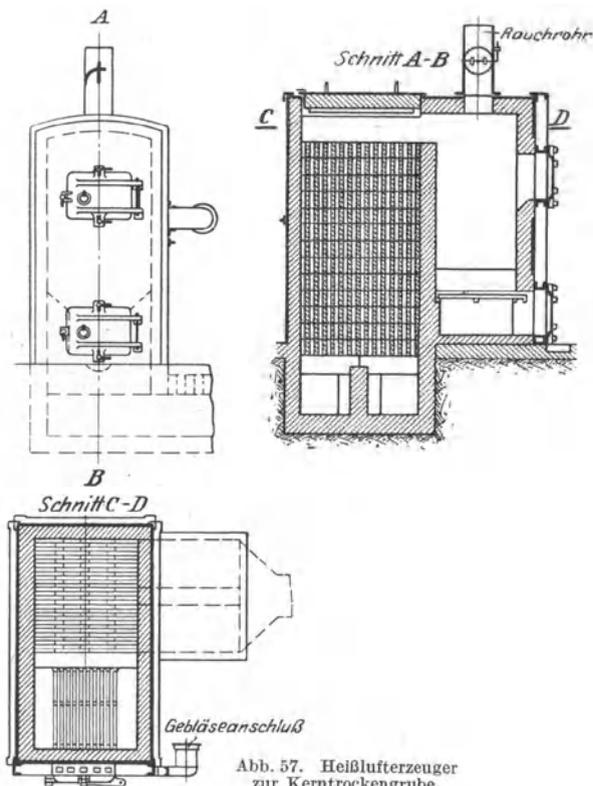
Heißlufterzeuger zur Kerntrockengrube.
